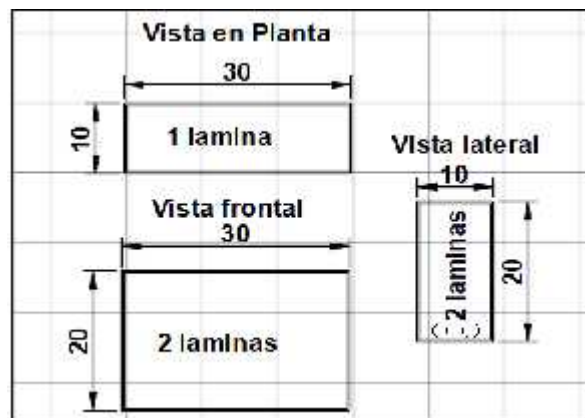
Planos para caja rectangular, dimensiones en [cm]
